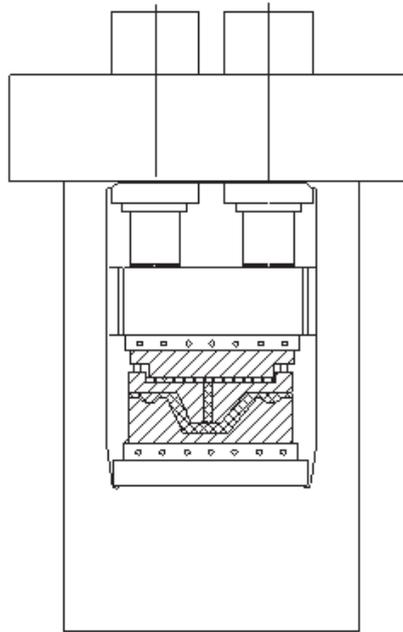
Presse zum Spritzpressen mit Formmasse im formgebenden Hohlraum
